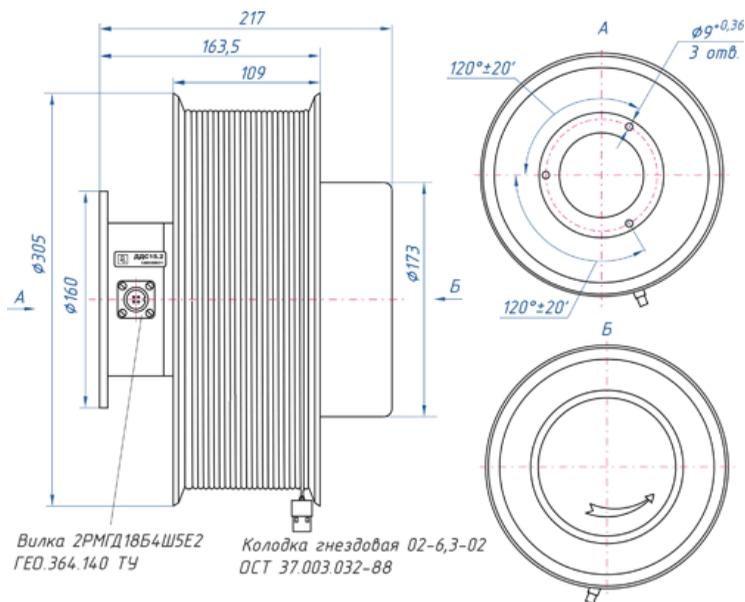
Габаритные и присоединительные размеры датчика длины стрелы
